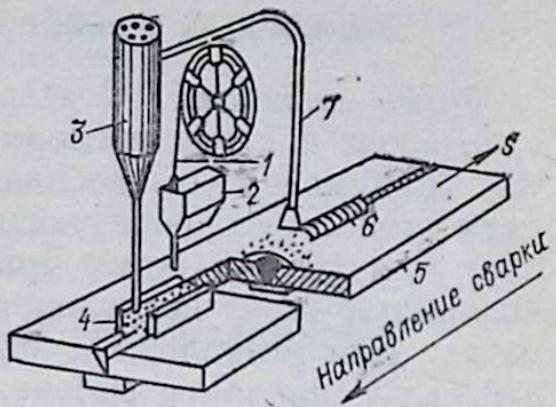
Схема дугосварочной автоматической установки для электрической сварки под слоем флюса:
